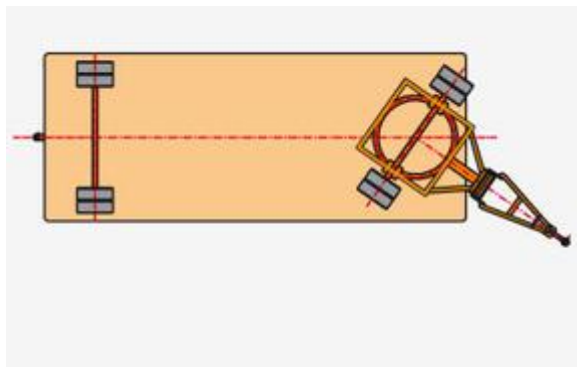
Поворотное устройство тележки с обеспечивающие поворот оси с колесами
